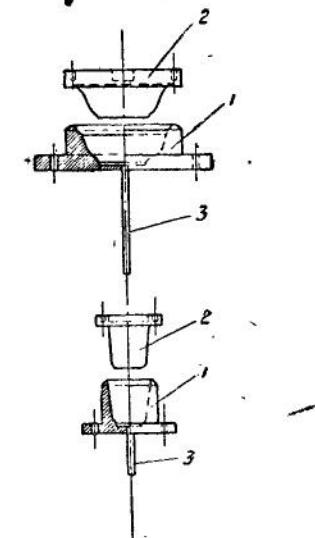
а. Чугунные формы для прессования миски (вверху) и чаши (внизу)
